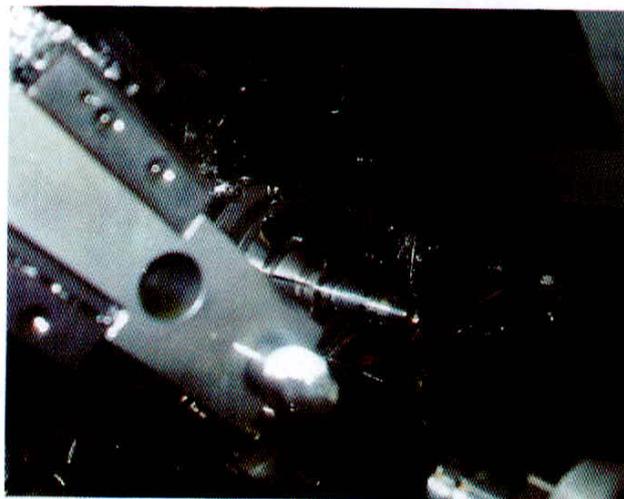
Porta Ferramentas do Torno Automático Multifuso CNC
